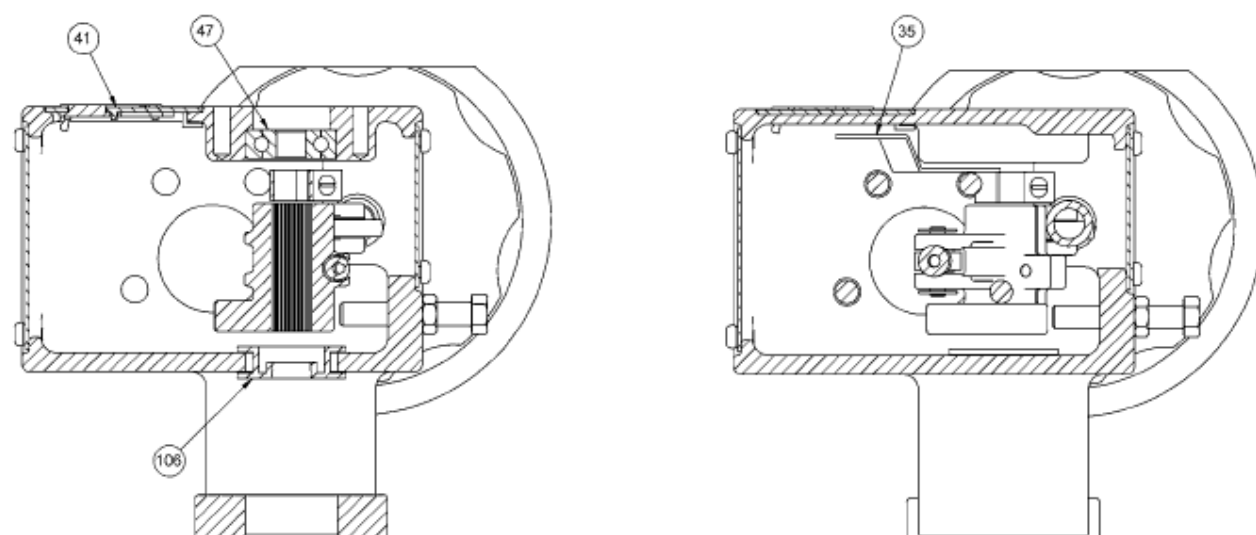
Привод размера AC, детализированный чертеж соединения
